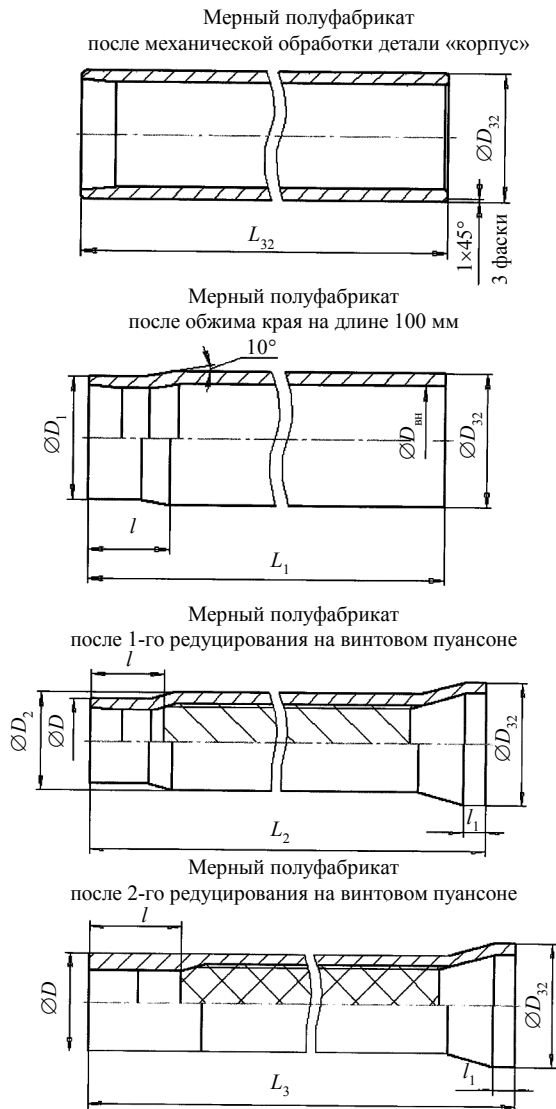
Схема прессовой технологии изготовления заготовки корпуса по технологическим переходам
